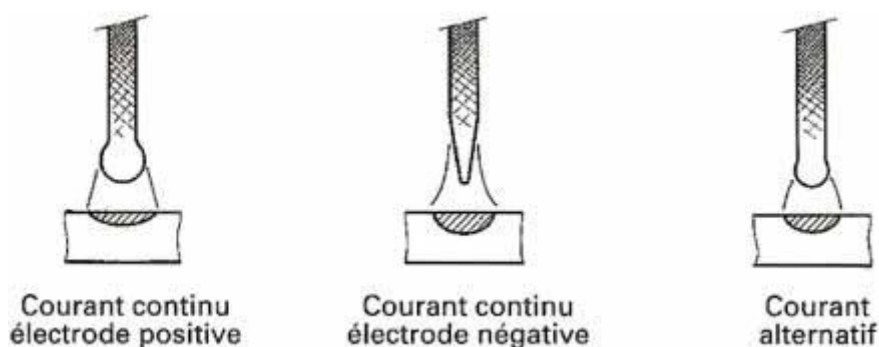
Forme des électrodes pour soudage TIG
